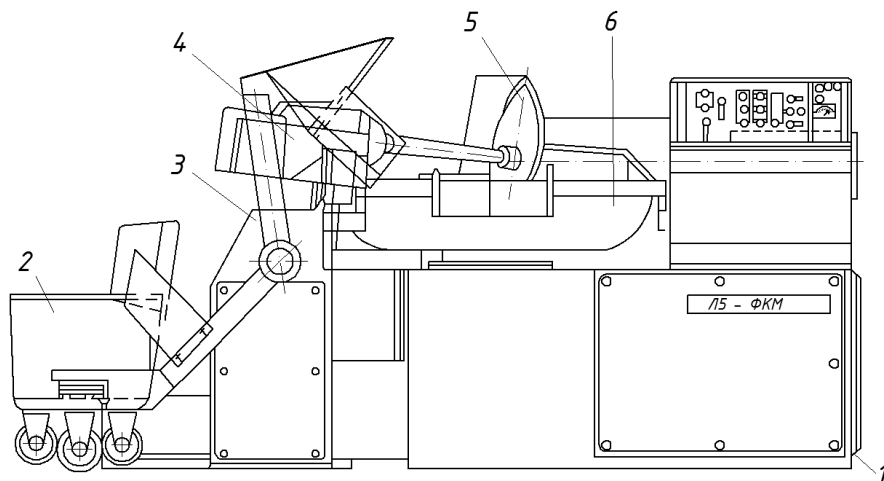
Куттер Л5-ФКМ: 1 - станина; 2 - тележка; 3 - механизм загрузки; 4 - выгрузатель; 5 - тарелка; 6 – чаша
